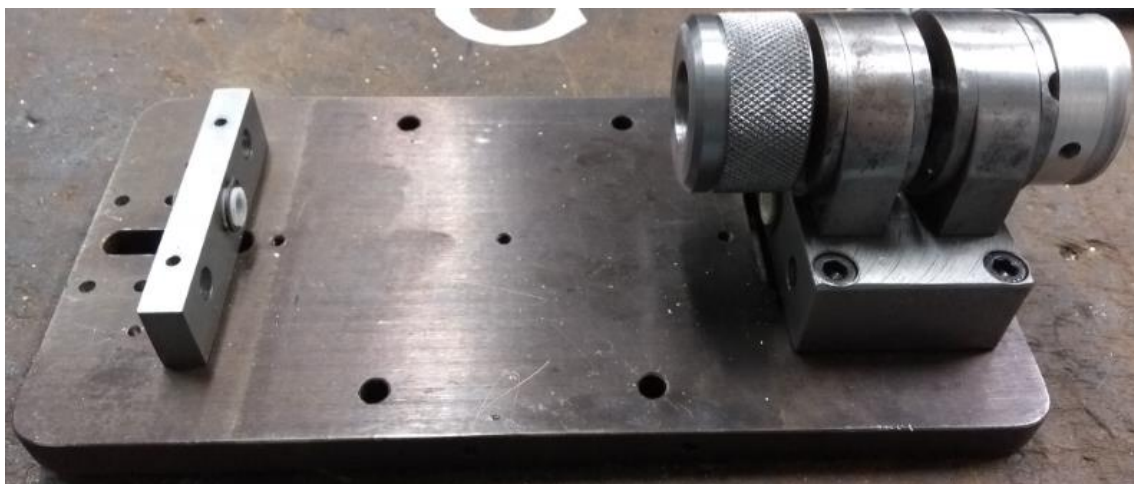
montagem do apoio das guias longitudinais e do cabeçote na placa
